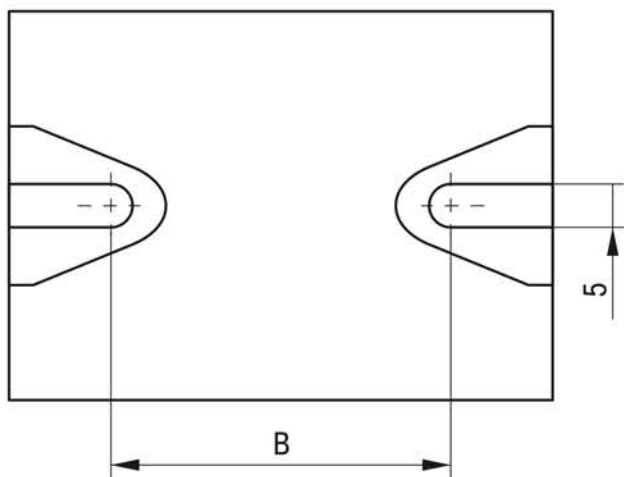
Установочные размеры шин / Figure 3 – Busbar mounting dimensions
